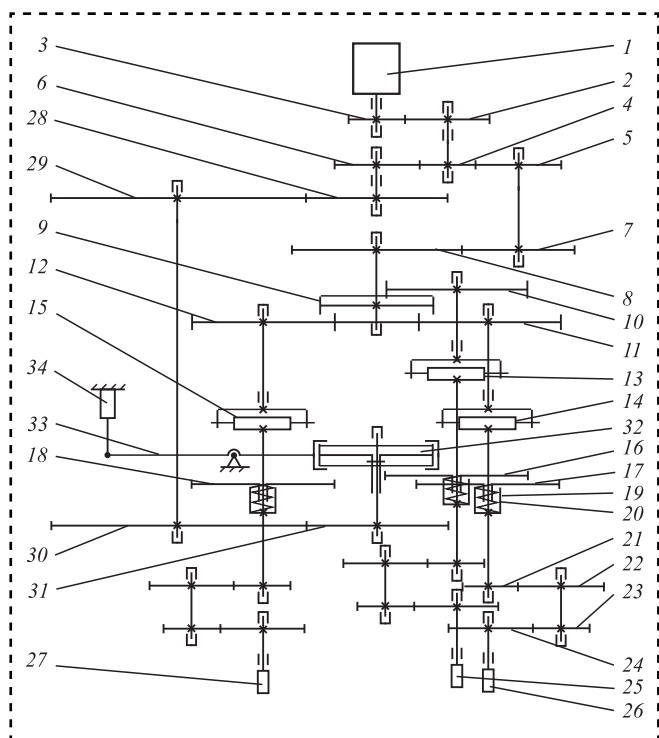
Кинематическая схема трехшпиндельного завинчивающего устройства
